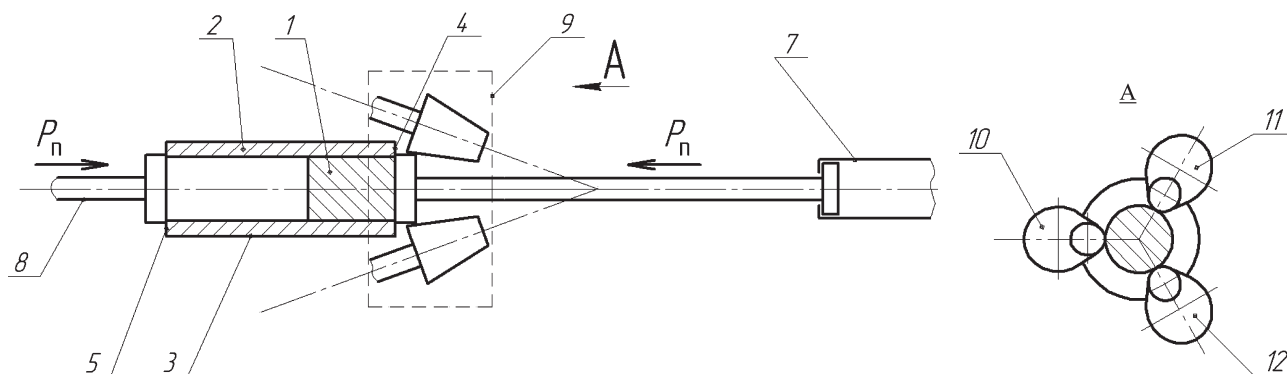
Схема трехвалкового стана прокатки коаксиальных слоистых металлических заготовок
